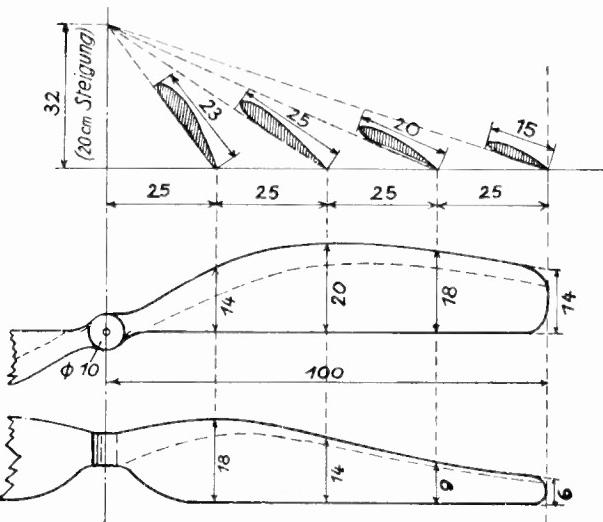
Luftschraubenentwurf. Radius 100 mm.
